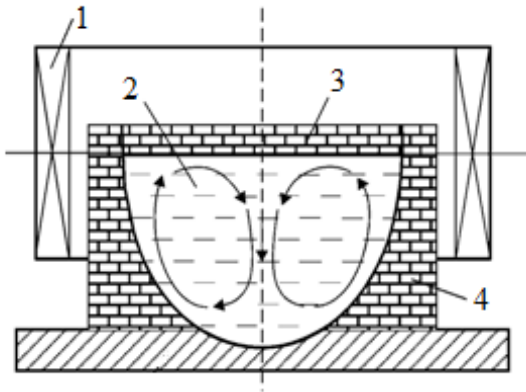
Схема движения макропотоков жидкого металла: 1 – индуктор; 2 – расплав; 3 – крышка; 4 – тигель [41]
